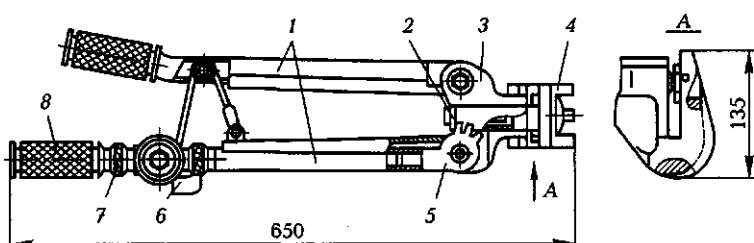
Пресс ручной механический для пробивки отверстий:
